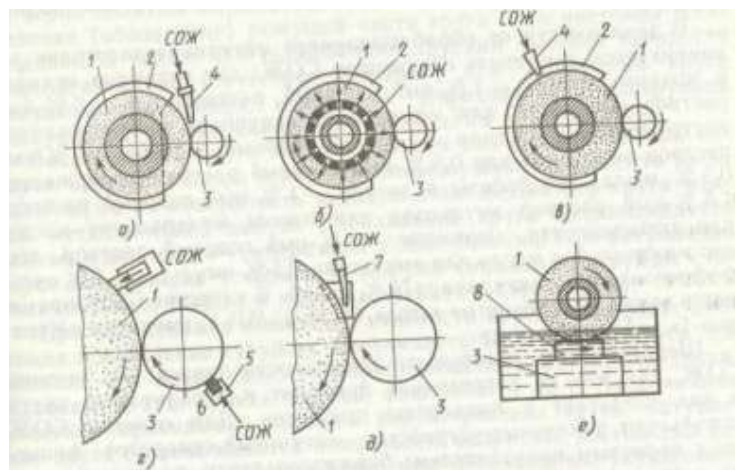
Схемы подачи СОЖ при шлифовании:
